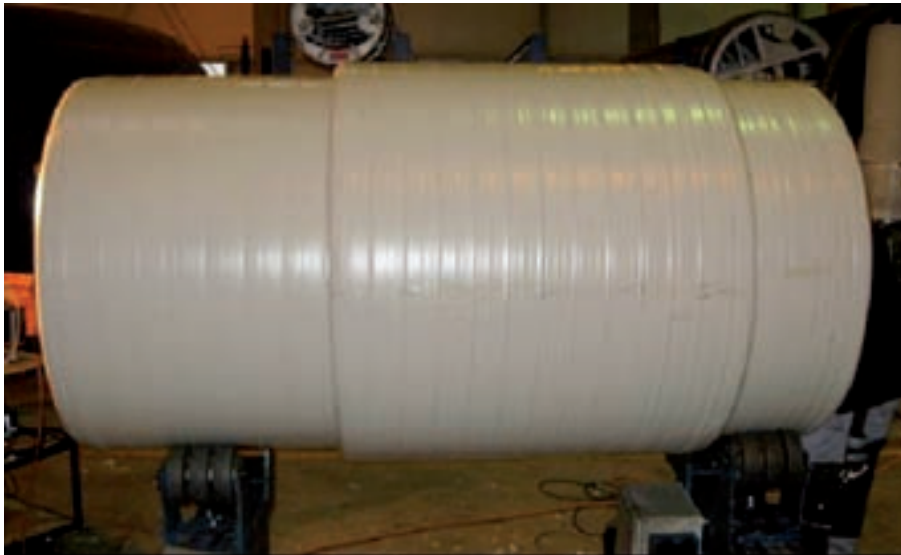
Wickelrohr mit Aufdickung als Halbzeug für ein mechanisch gefertigtes Formteil
